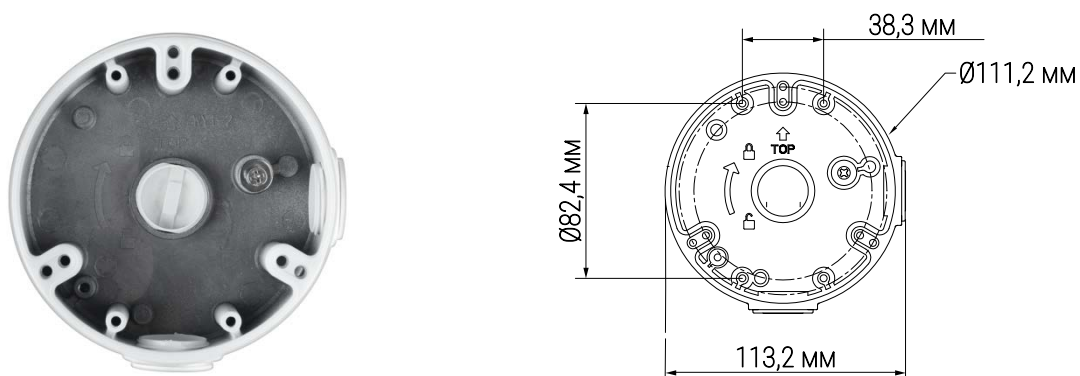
Габаритные размеры. Монтажная коробка BR-205
